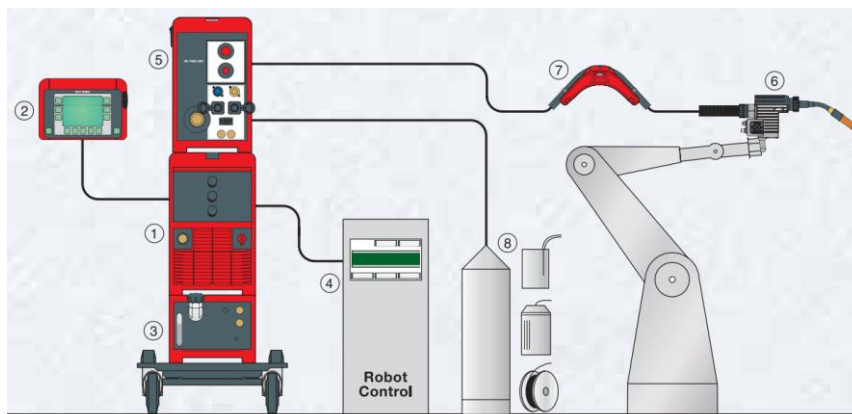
Principais componentes para a realização de soldagem CMT [61].
